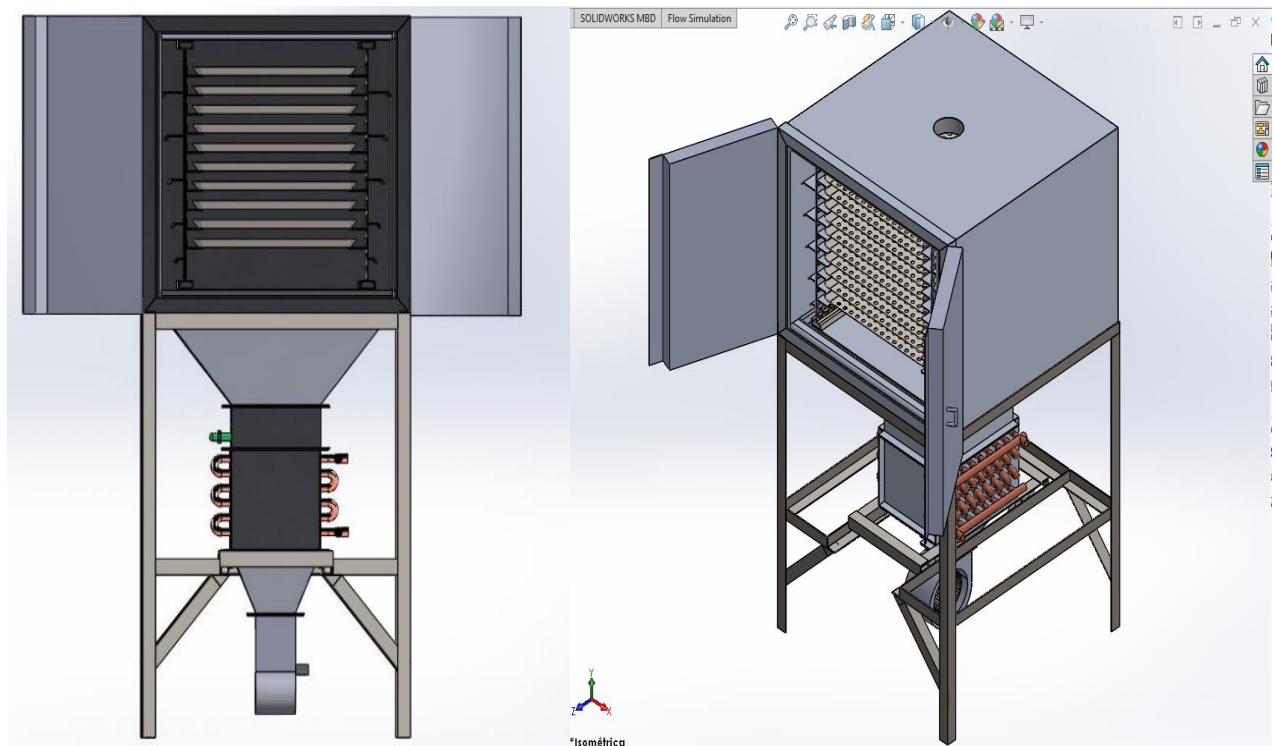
Vista frontal de la cámara de secado .Charolas, baffles y bastidores dentro de la cámara de secado (izquierda), Vista isométrica de la cámara de secado ensamblada con el intercambiador de calor de tubos aletados y el ventilador centrífugo (derecha) (Garduño Rodríguez, 2018)
